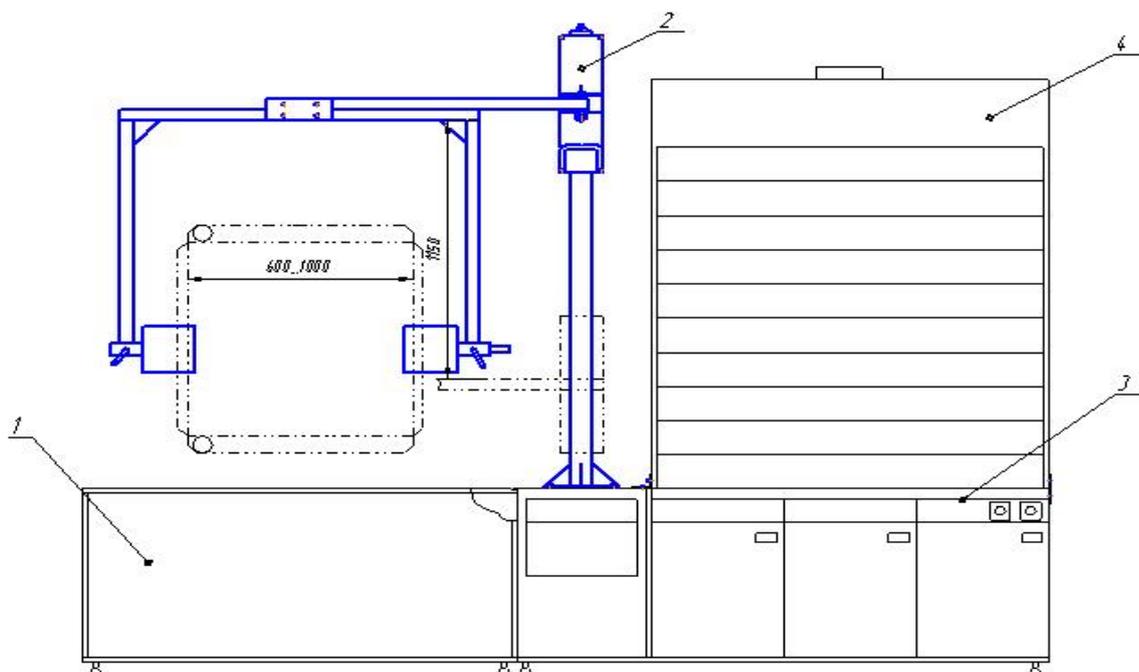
Приспособление для ремонта и испытания радиаторов
